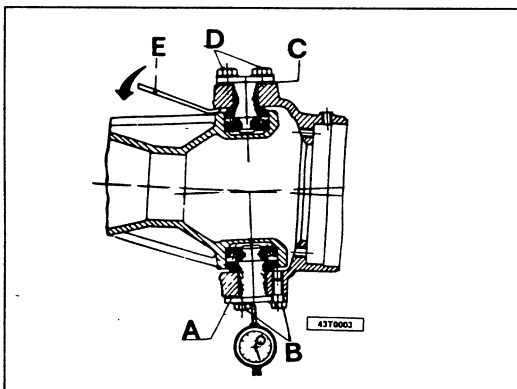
Medición del juego de los cojinetes de las horquillas.
